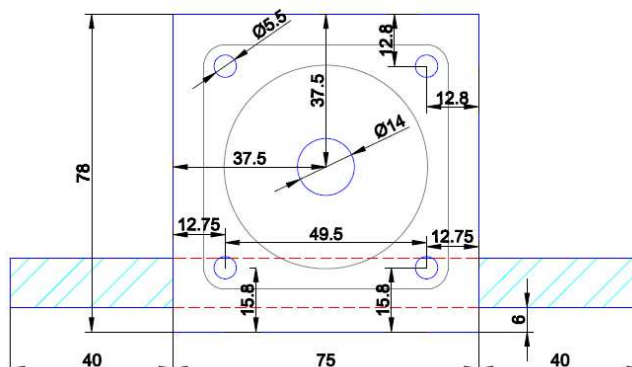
Vista de frente, flange de acoplamento do servomotor à mesa/guia. Visualização do AutoCad.
